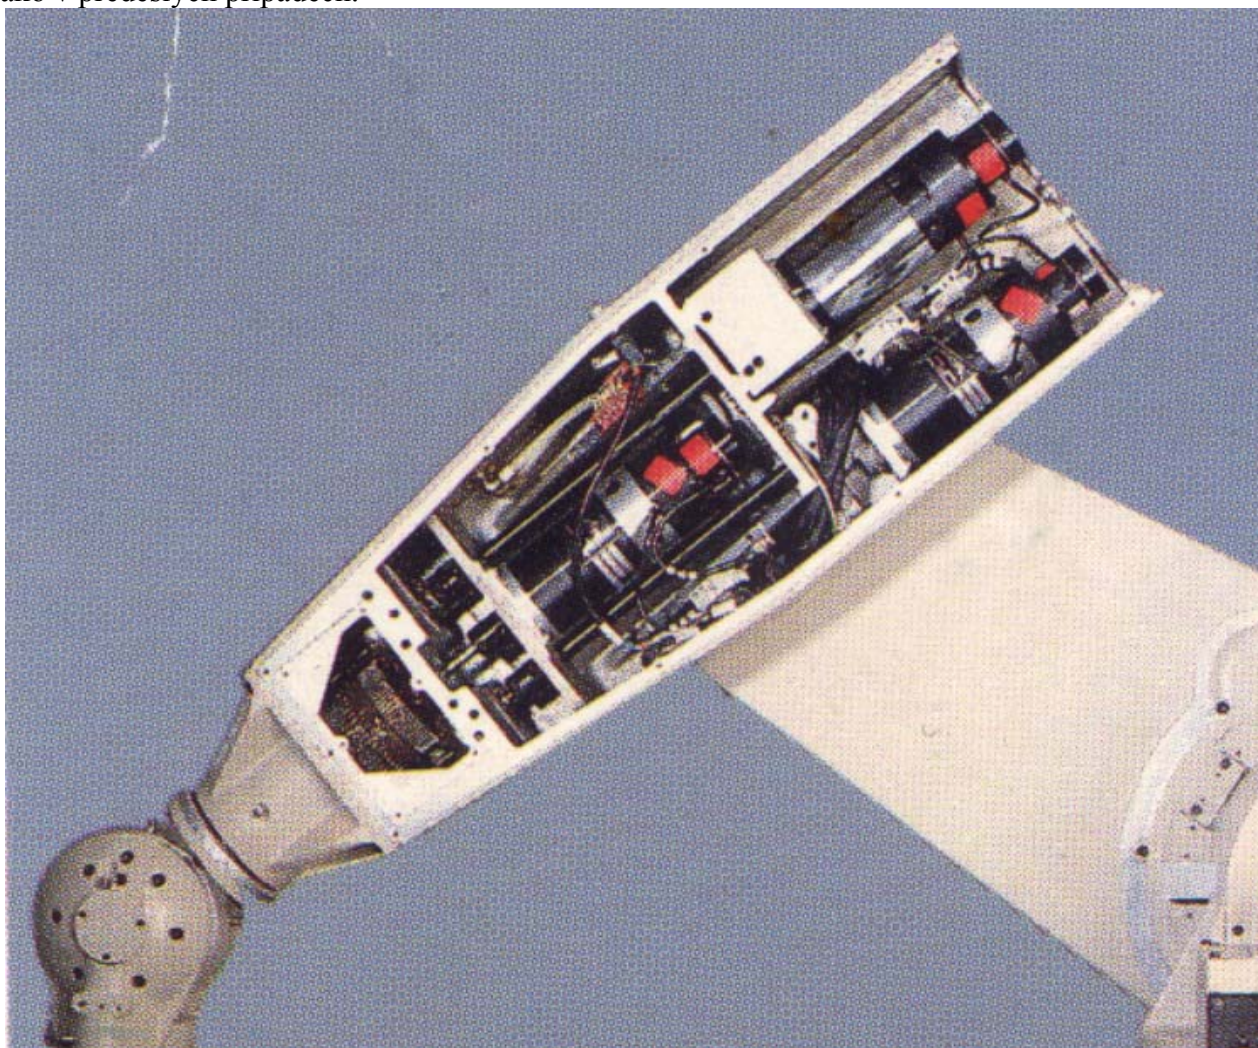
5 Konstrukce prvního stupně volnosti
